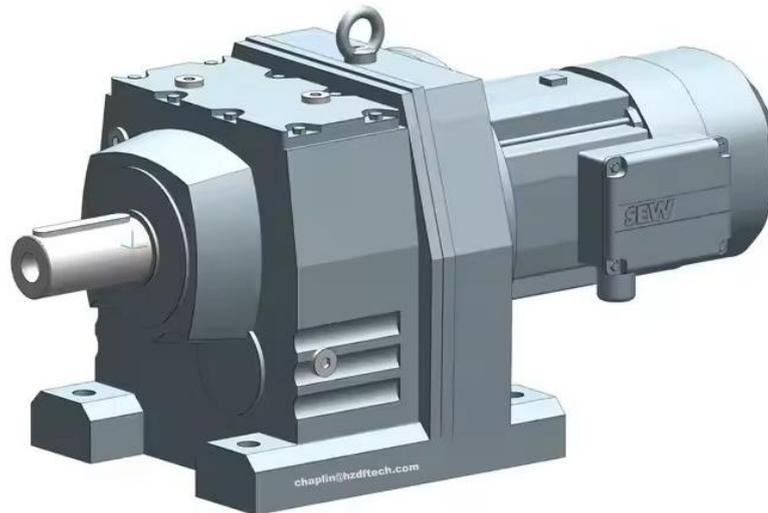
Мотор-редуктор SEW серии R97 с фланцевым креплением
